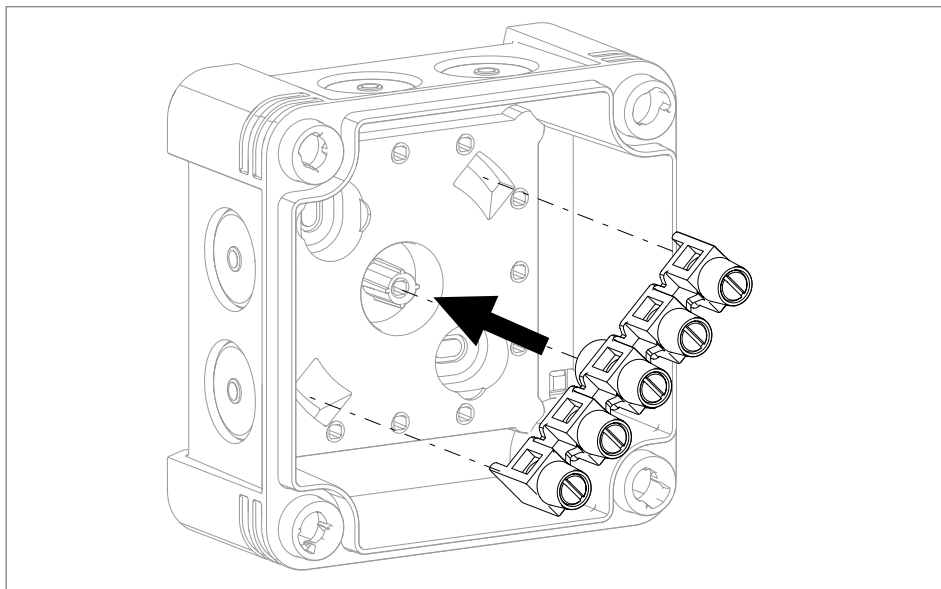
Enfichage d'un bornier de raccordement de type 689 dans la boîte de dérivation
